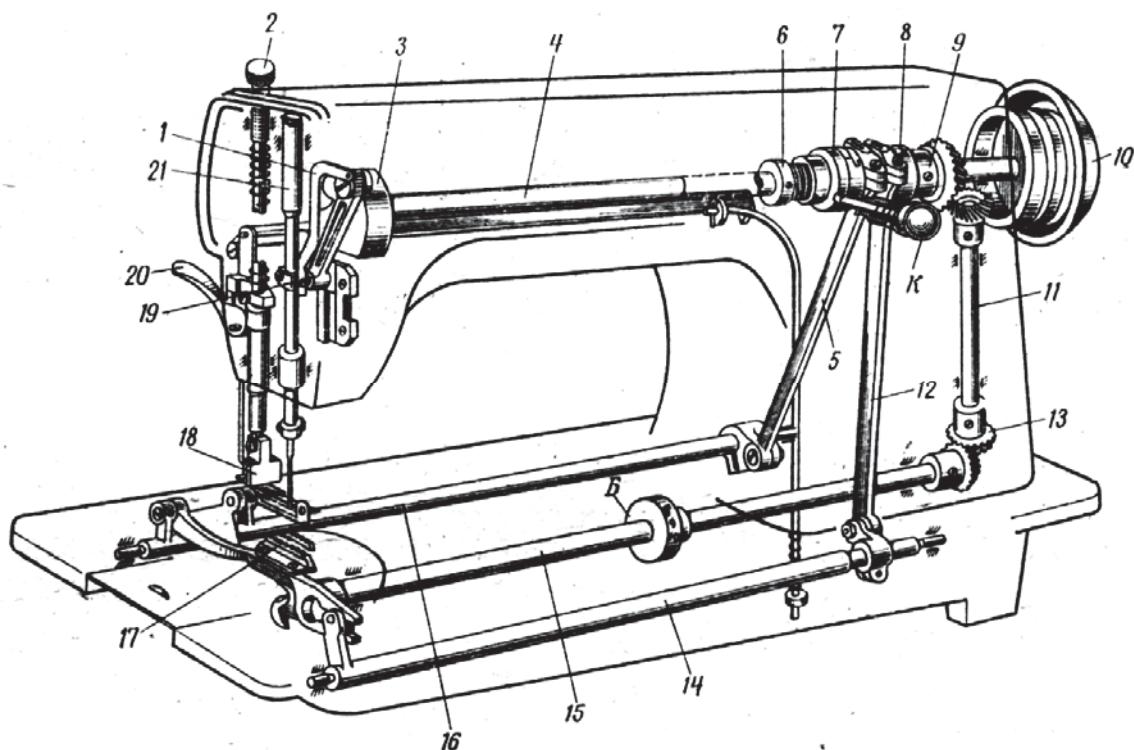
Конструктивно-кінематична схема механізмів швейної машини 2222-М кл:
